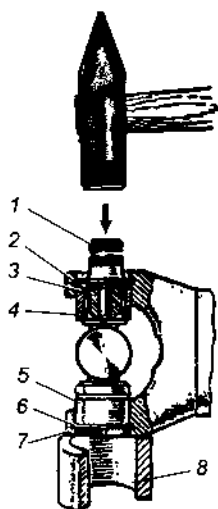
Разборка карданного вала: 1 — оправка; 2 — игольчатый подшипник; 3 — крестовина; 4 — уплотнительная манжета; 5 — стакан; 6 — стопорное кольцо; 7 — пыльник; 8 — кольцо
